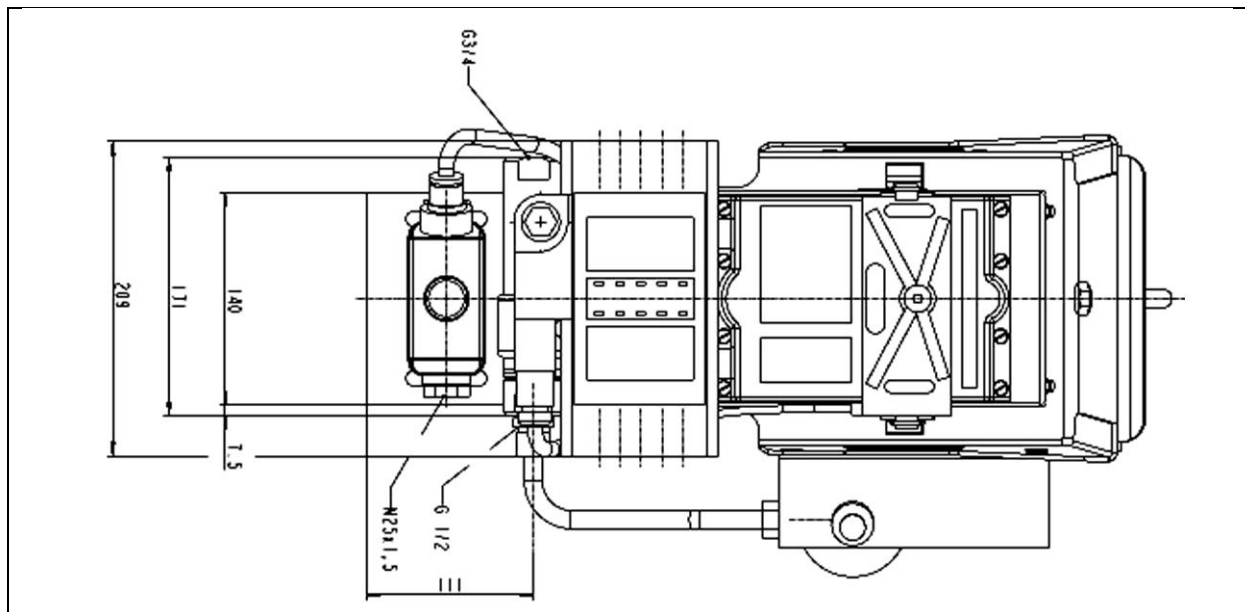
Mechanische Abmessungen des VN215/87plus: Draufsicht
